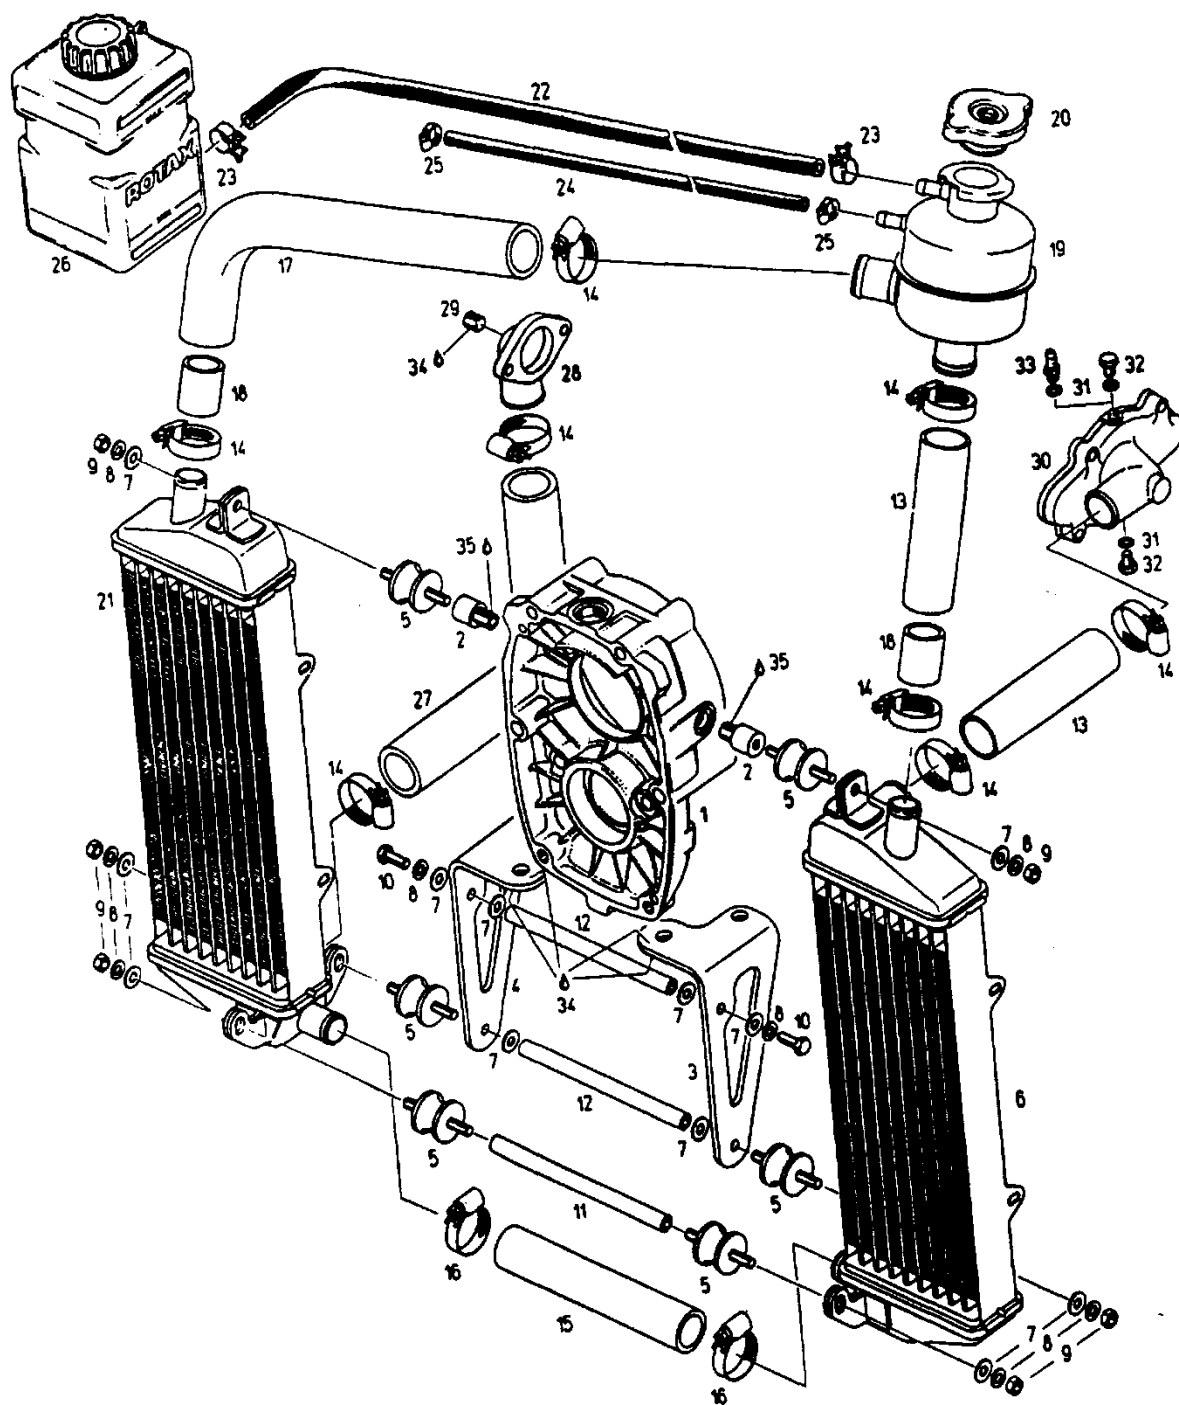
Двухсекционный высокий радиатор для двигателя, установленного свечами вниз
